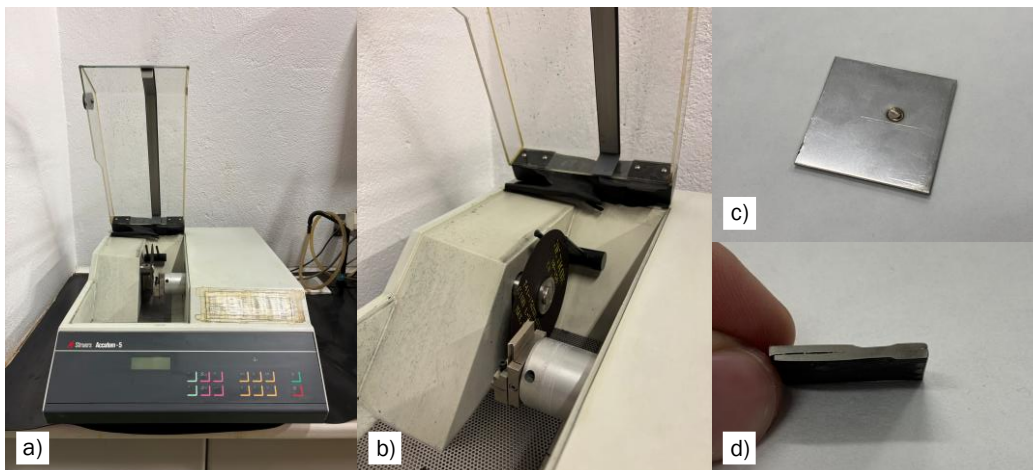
(a) Tronzadora (b) Detalle disco de corte (c) Muestra soldada (d) Corte longitudinal de las chapas para su posterior empastillado
